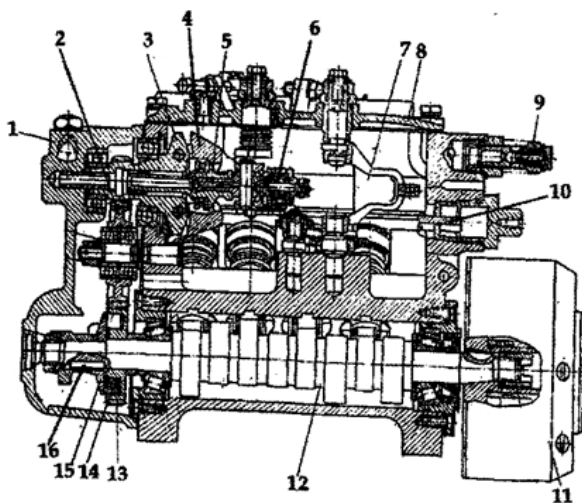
Топливный насос высокого давления: 1 - задняя крышка регулятора; 2 - промежуточная шестерня регулятора; 3 - державка грузов; 4 - груз; 5 - муфта грузов; 6 - корректор; 7 - рычаг пружины; 8 - верхняя крышка; 9 - редукционный клапан; 10 - рейка; 11 - муфта опережения впрыска топлива; 12 - кулачковый вал; 13 - ведущая шестерня регулятора; 14 - сухарь; 15 - фланец.
